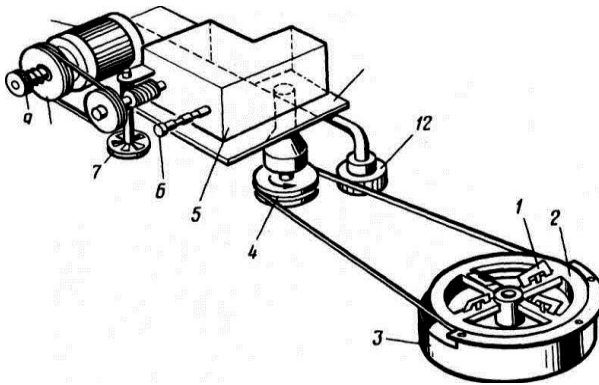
Універсальний ріжучий механізм УРМ: 1 - ніж; 2, 4 - шків; 3 - огороження; 5 - коробка швидкостей; 6 - рукоятка; 7 - штурвал; 8 - варіатор; 9 - гайка; 10 - електродвигун; 11 - рама; 12 - ролик
